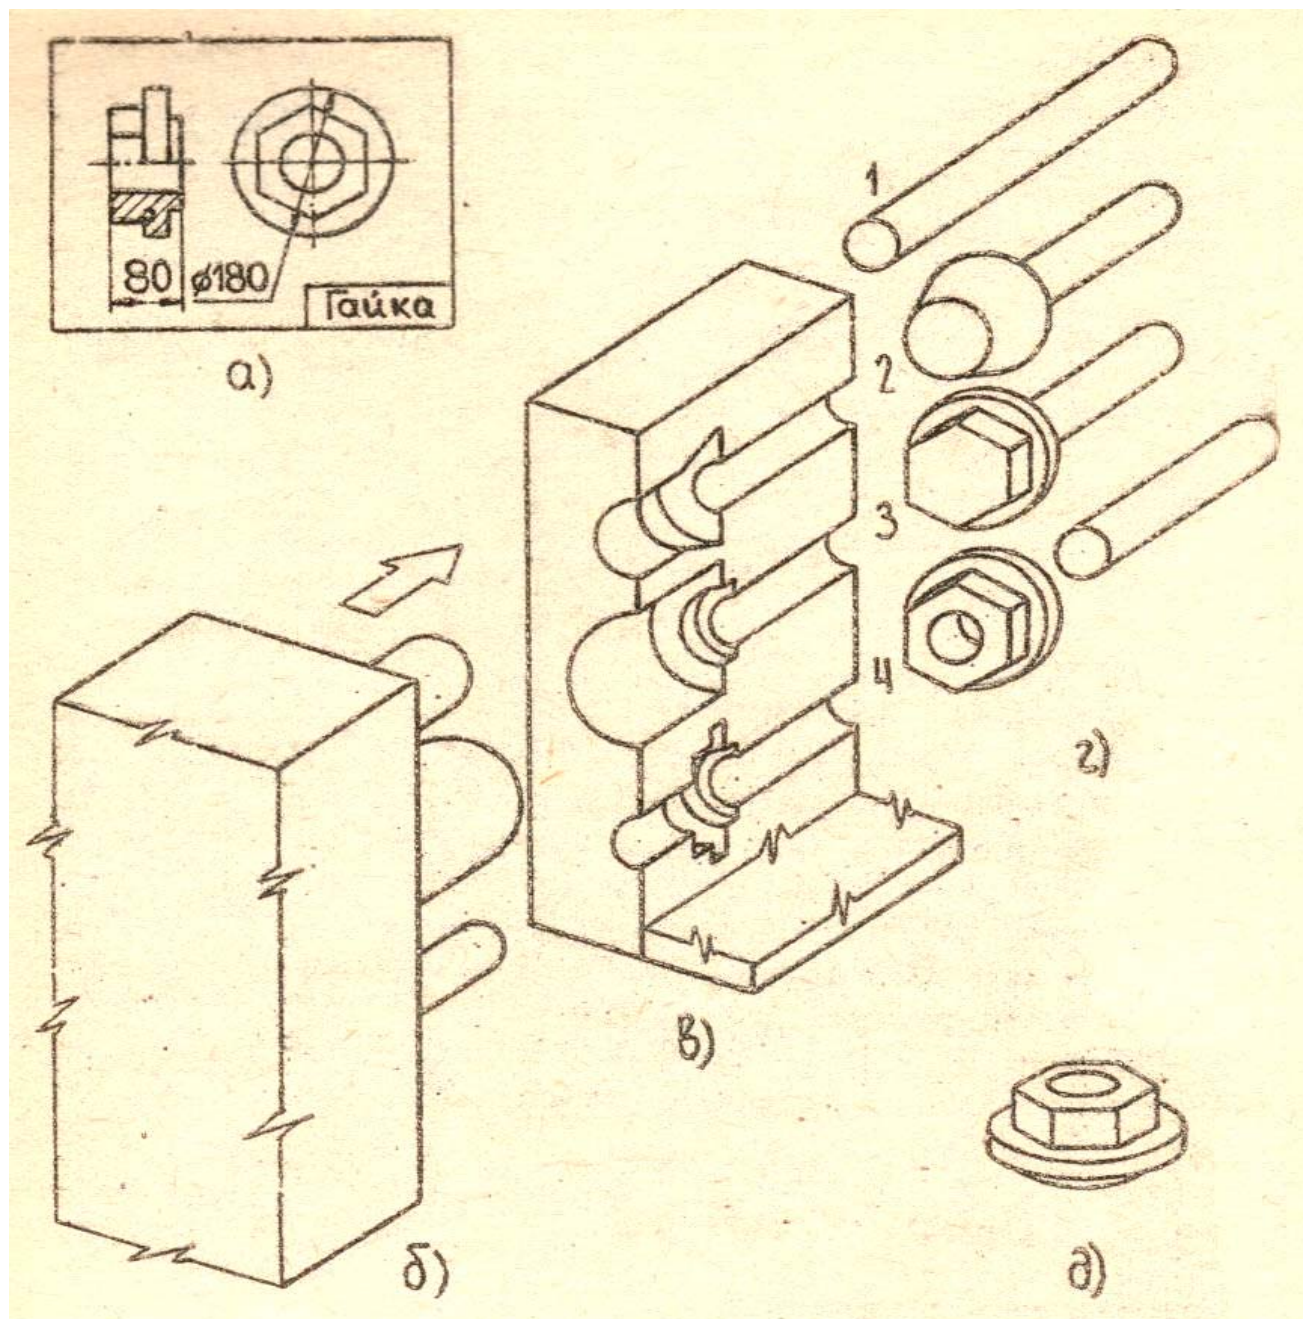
Конструкция штампа и схема штамповки на ГКМ: а — чертеж поковки; б — блок пуансонов; в — неподвижная матрица (подвижная матрица частично удалена); г — переходы штамповки; д — поковка; 1 — исходная заготовка; 2 — набор металла, высадка конуса; 3 — формирование поковки; 4 — прошивка отверстия и отделение поковки от заготовки
